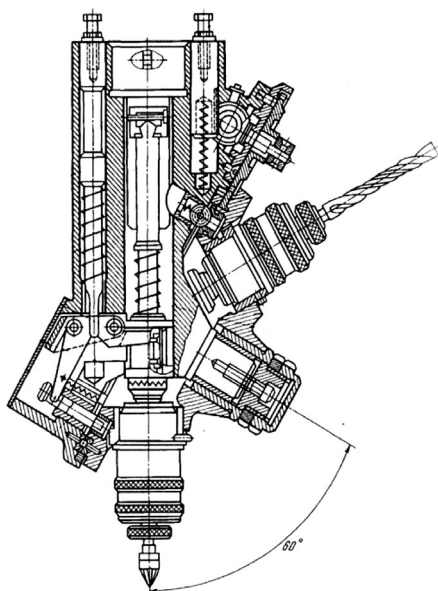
Револьверная шестишпиндельная головка вертикально-сверлильного станка [8]
